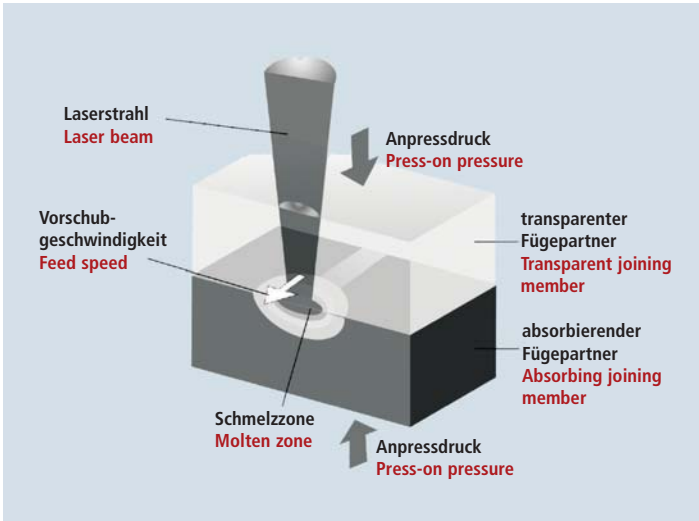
Laserstrahlschweißen in Durchstrahltechnik
